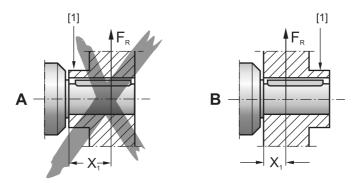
Disposição da montagem de uma engrenagem ou pinhão para corrente
